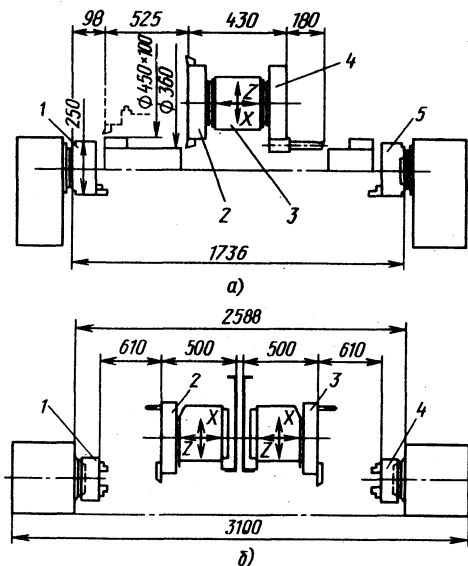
Расположение шпинделей и суппорта с револьверными головками в токарных станках с ЧПУ фирмы Biglia (Италия):
